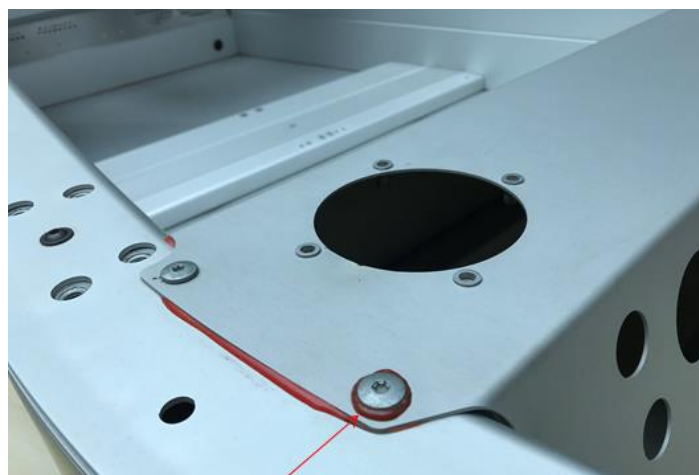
Tornillos autorroscantes y adhesivos en una carrocería de automóvil. Fuente: TWI
